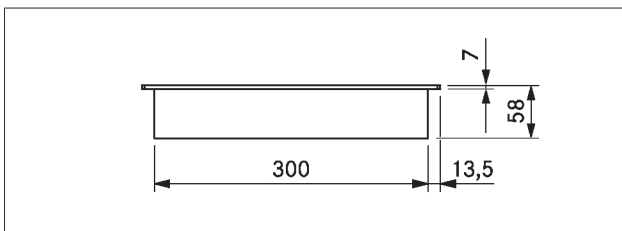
Dimensões do aparelho CKFI, vista frontal
